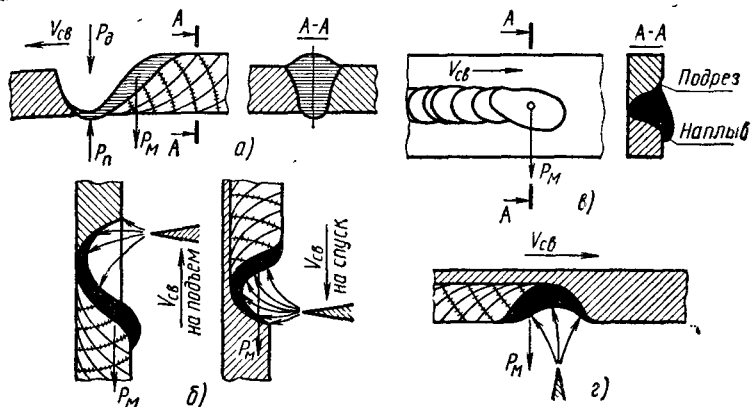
Схема сил, действующих в сварочной ванне, и формирование шва в разных пространственных положениях:
